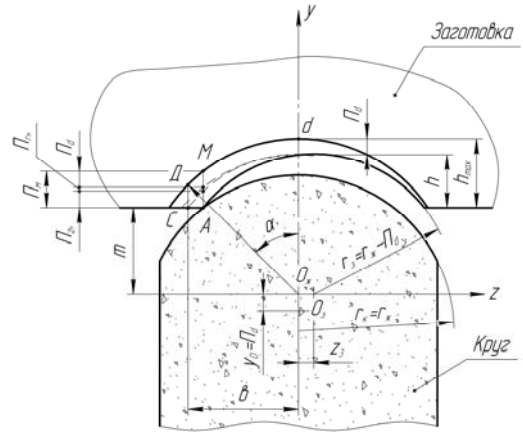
Схема контакта шлифовального круга и заготовки в начале обработки
